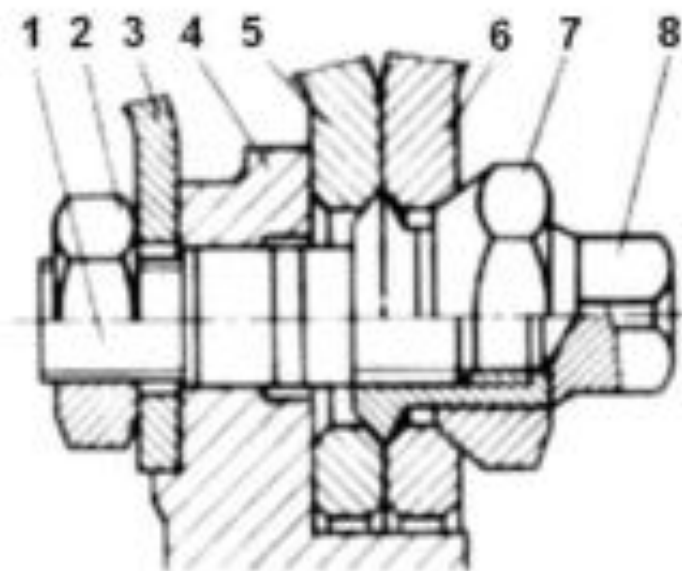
Крепление колеса легкового автомобиля.
